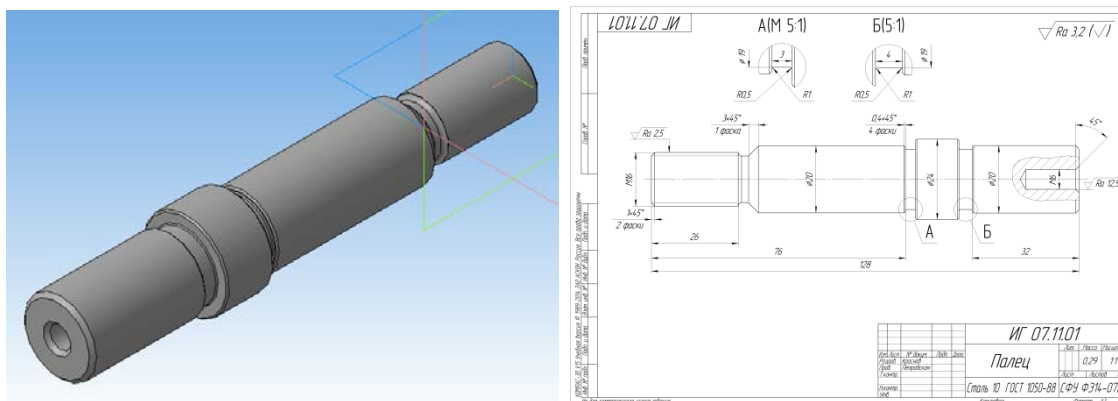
3D-модель детали и полученный с неё рабочий чертёж
